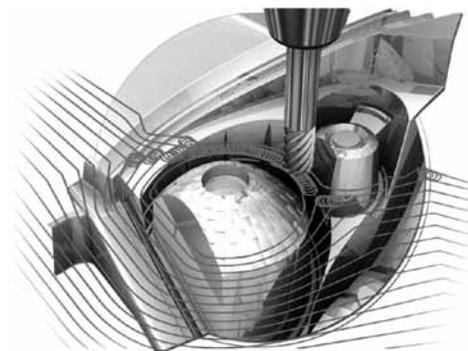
Трохоидальная обработка позволяет избежать фрезерования с большой нагрузкой
